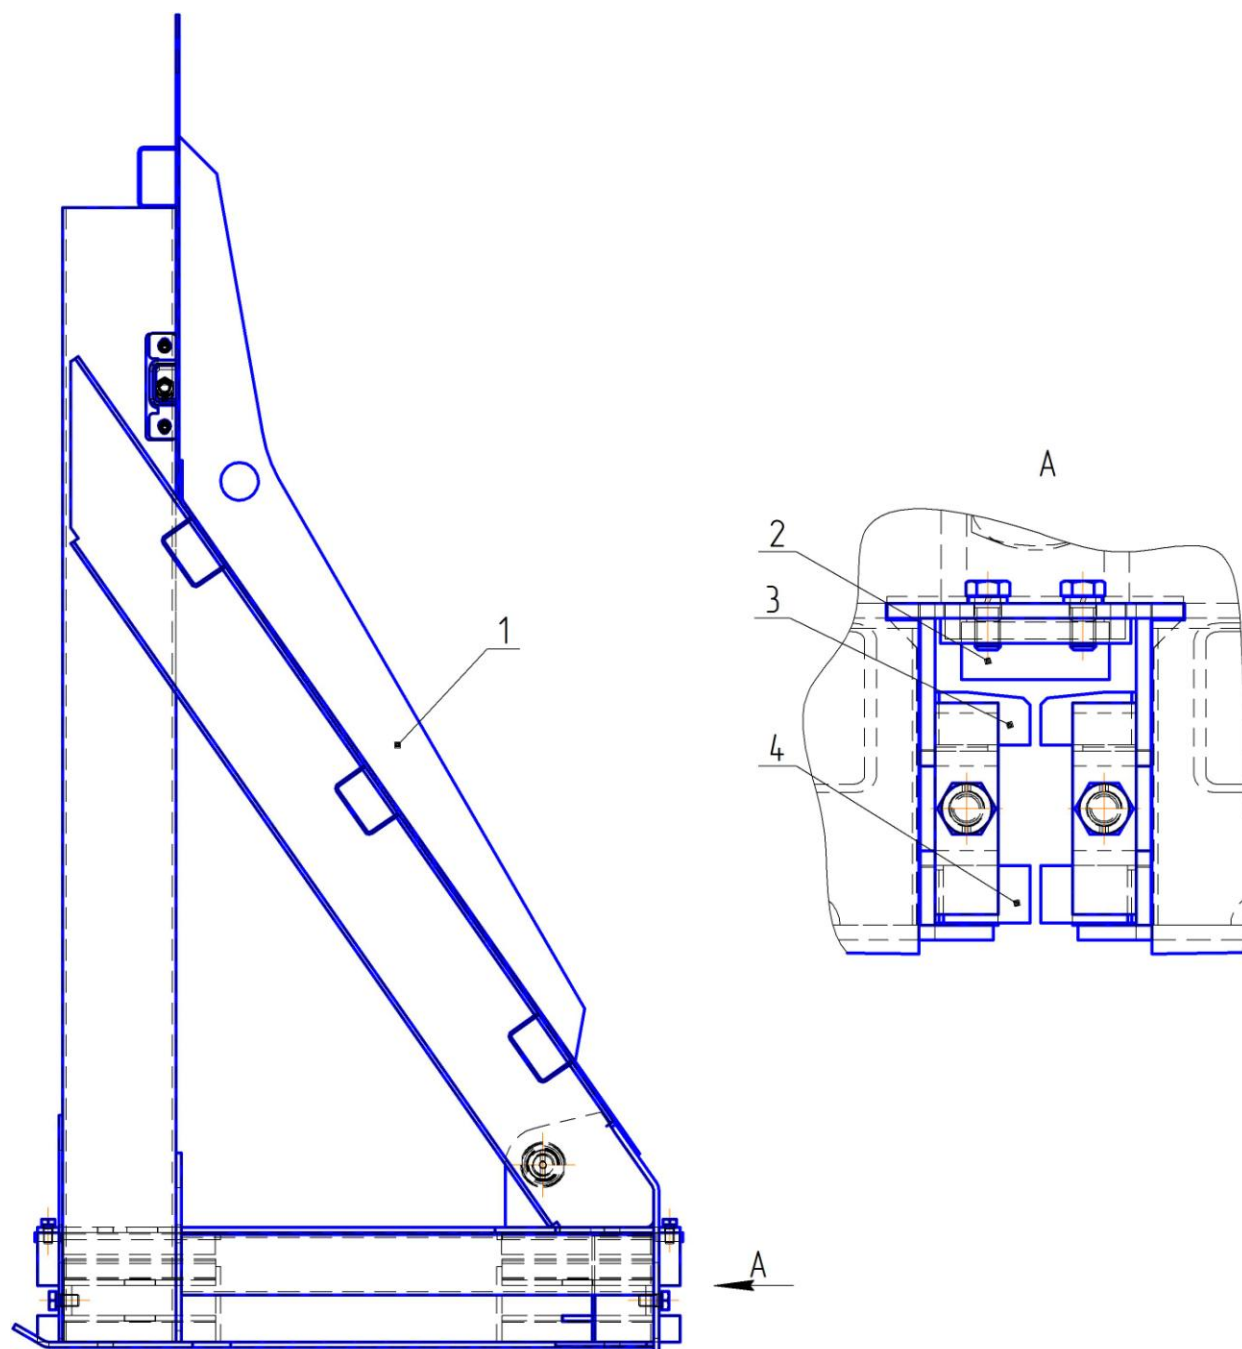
Плита выталкивающая для мусоровоза КО-456-20
